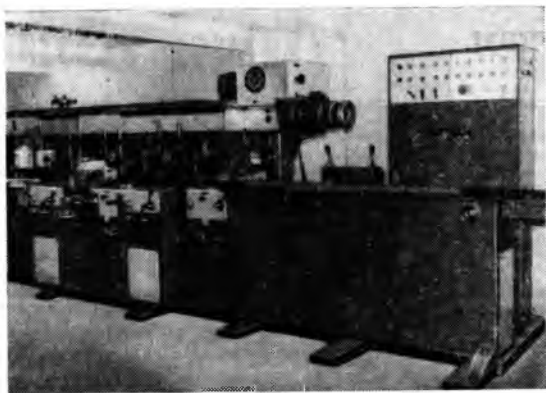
Четырехсторонний фрезерный станок ФП-160
